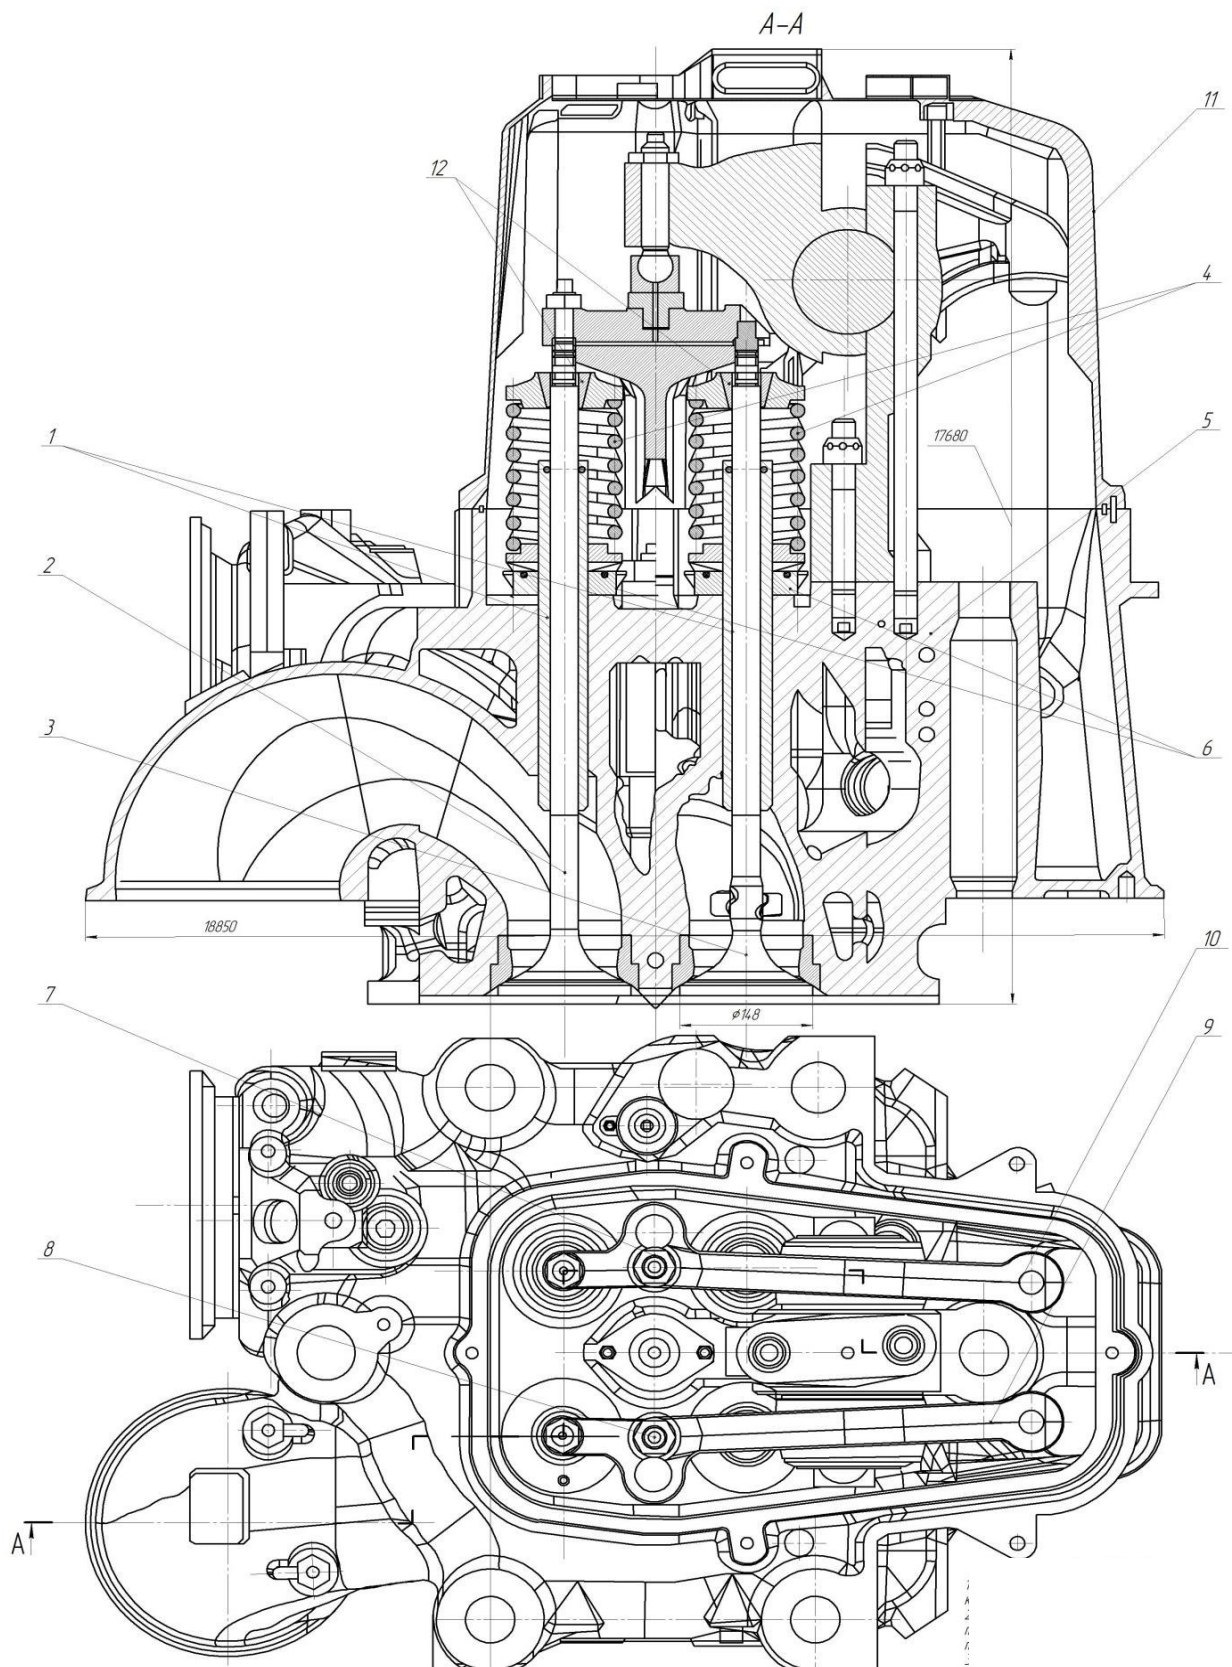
Компонування деталей газорозподільного механізму у головці циліндра суднового двигуна МаК 8М43С: 1 – втулка клапана; 2 – впускний клапан; 3 – випускний клапан; 4 – пружина; 5 – корпус головки циліндрів; 6 – механізм повороту клапана; 7 – комплект випускного клапана; 8 – комплект впускного клапана; 9 – рокер впускного клапана; 10 – рокер випускного клапана; 11 – кришка головки циліндра; 12 – затискний конус
